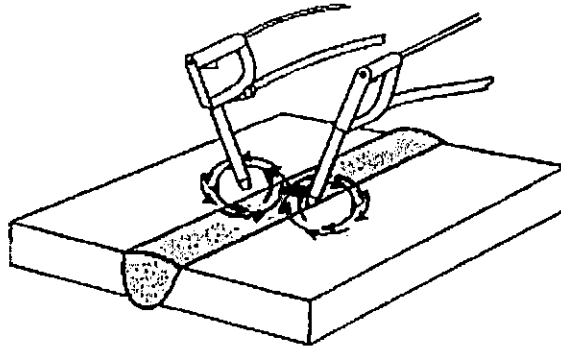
Representación Esquemática de la aplicación de una prueba de partículas magnéticas a una unión soldada. Nótese la posición de las puntas con el fin de detectar defectos en la zona de la junta soldada ubicada entre y en las inmediaciones de las puntas. ^[1-30]
